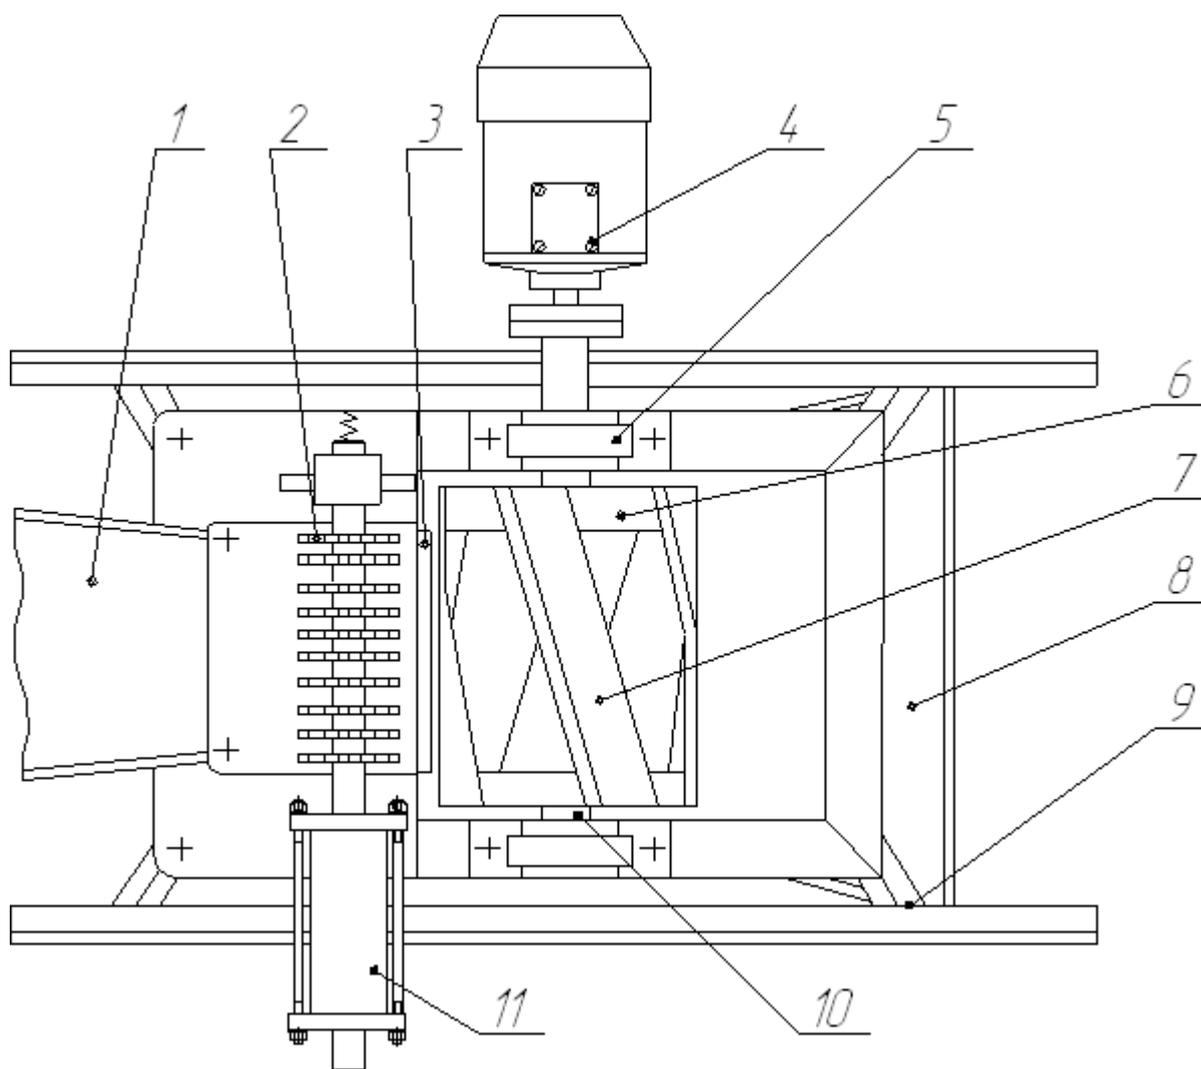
Конструкция измельчителя листостебельных кормов с безредукторным электроприводом: 1 — загрузочный лоток; 2 — направляющий рассекаль; 3 — противорежущая пластина; 4 — асинхронный электродвигатель; 5 — корпус шарикоподшипника вала барабана; 6 — диск режущего барабана; 7 — нож; 8 — выгрузной лоток; 9 — станина; 10 — вал барабана; 11 — линейный асинхронный электродвигатель.
